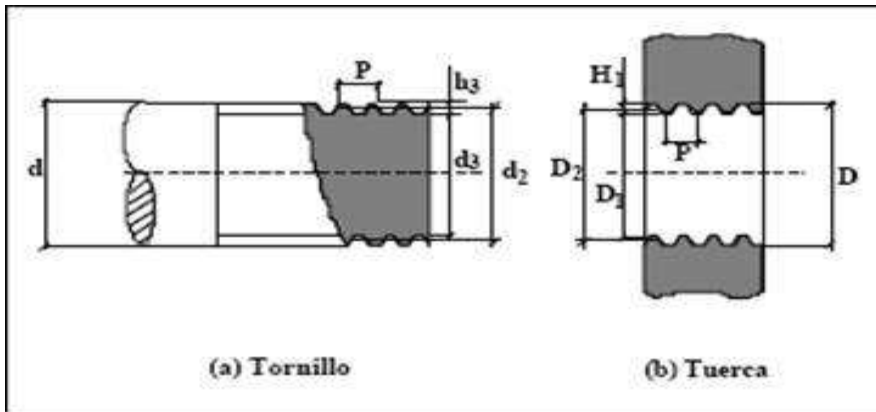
Dimensiones principales en tornillos y tuercas, fuente: internet
